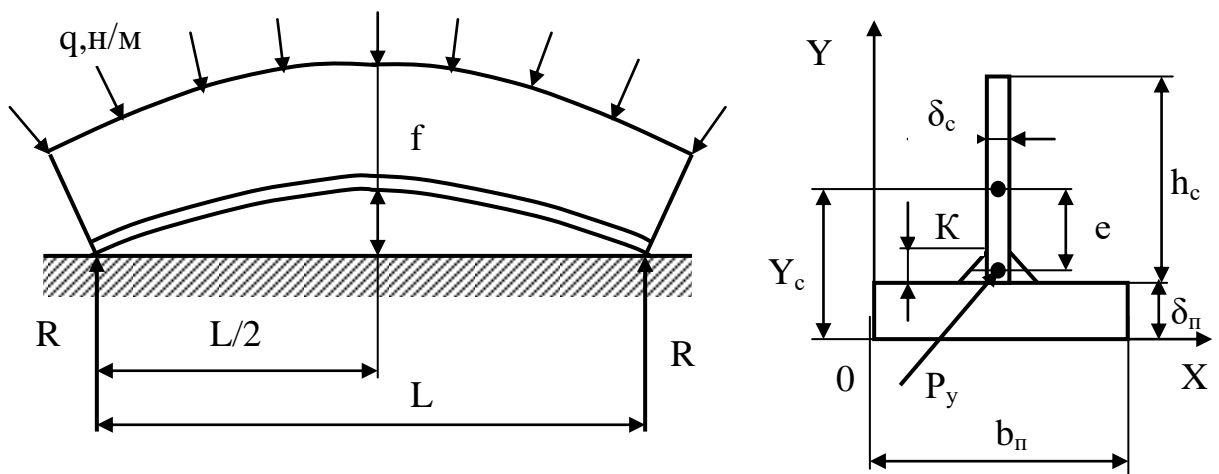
Розрахункова схема притиску заготовок балки в кондукторі рівномірно розподіленими силами
